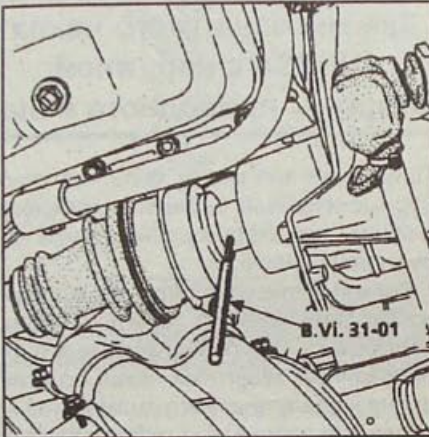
Использование борodka B.Vi.31-01 для выбивания упругого штифта правого приводного вала коробки передач JC5
